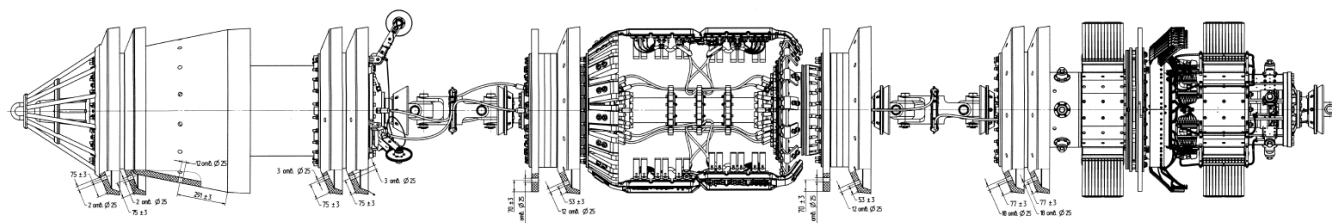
Чертеж общего вида дефектоскопа внутритрубного комбинированного магнитно-ультразвукового 40-ДМУ.01-00.000 в типоразмере 1020 мм (40")
